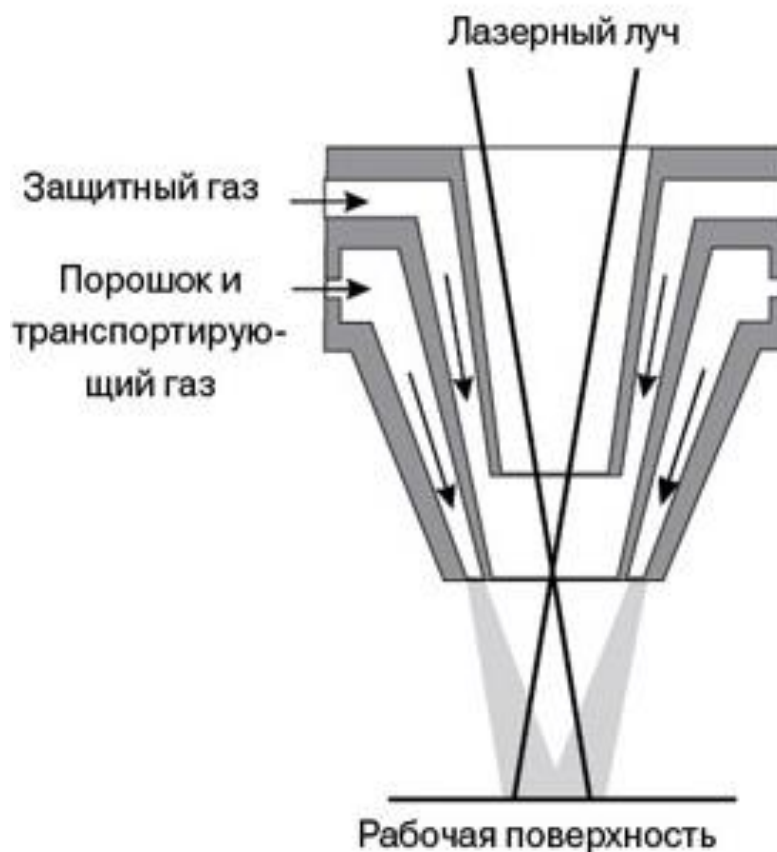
Схема наплавки с коаксиальной подачей порошка
